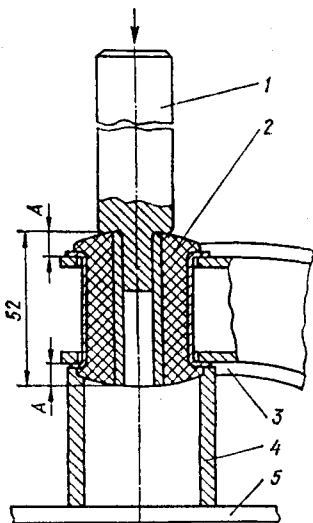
Выпрессовка сайлентблока из рычага передней подвески: 1 – оправка; 2 – сайлентблок; 3 – рычаг; 4 – подставка; 5 – основание
